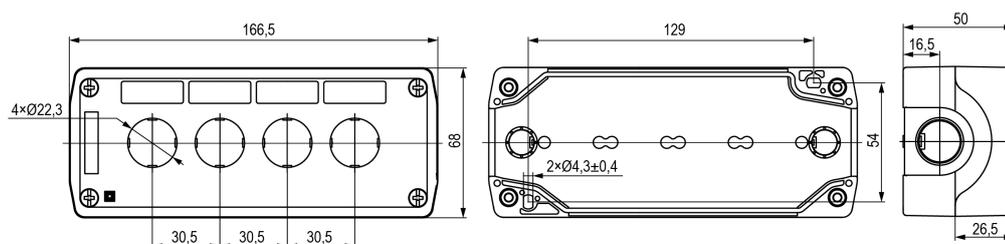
Габаритные и установочные размеры четырехместного корпуса
